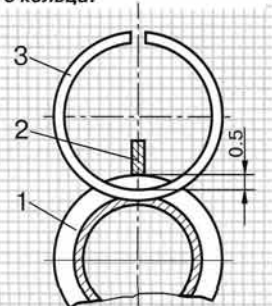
Проверка соответствия поршневого кольца глубине канавки поршня: 1 — поршень; 2 — линейка; 3 — поршневое кольцо.
